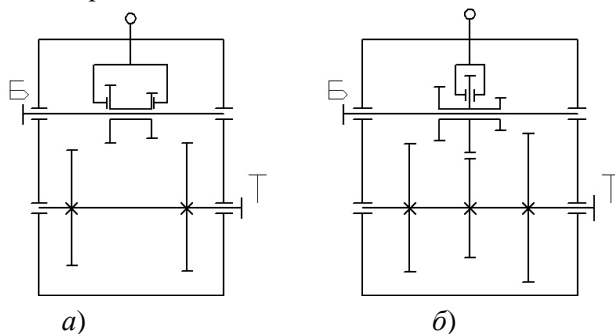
Коробки передач: а – с двойным блоком; б – с тройным блоком.
